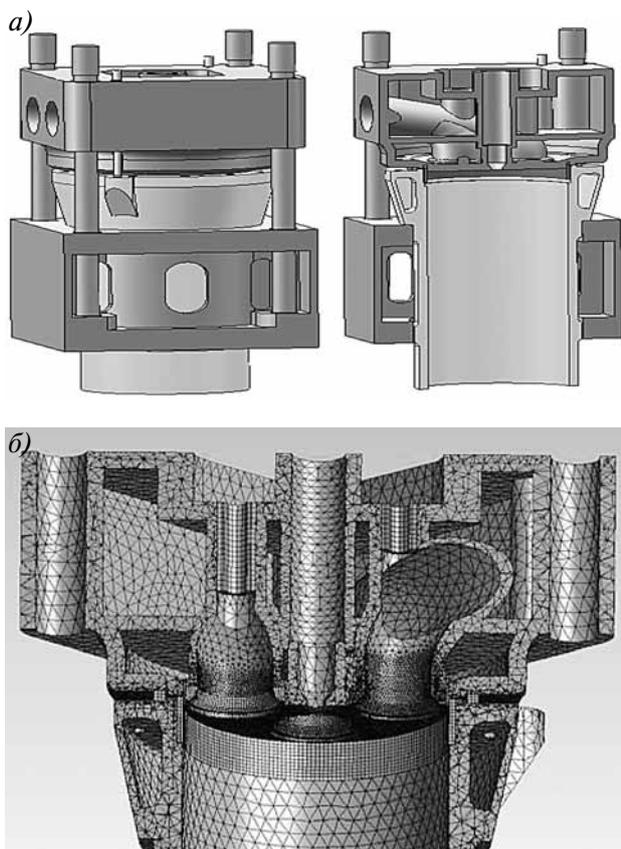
Твердотельная (а) и конечно-элементная модель (б) сборки блока, втулки и крышки цилиндра двигателя типа ЧН26,5/31
